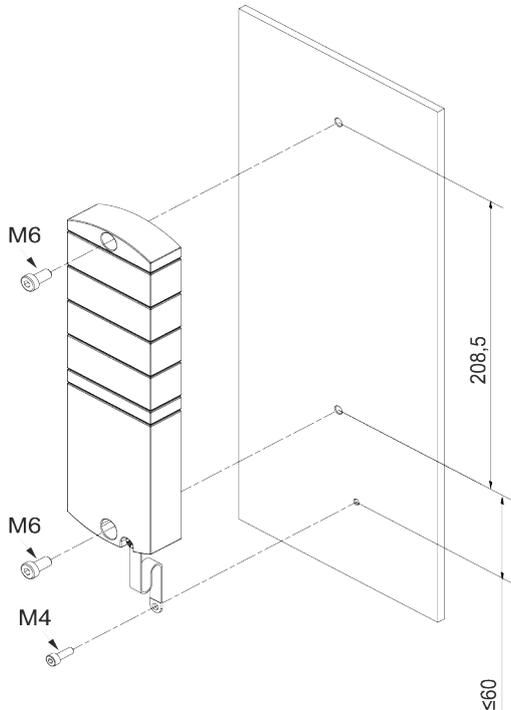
Gerät befestigen. Abmessungen in mm (Abbildung ähnlich)
